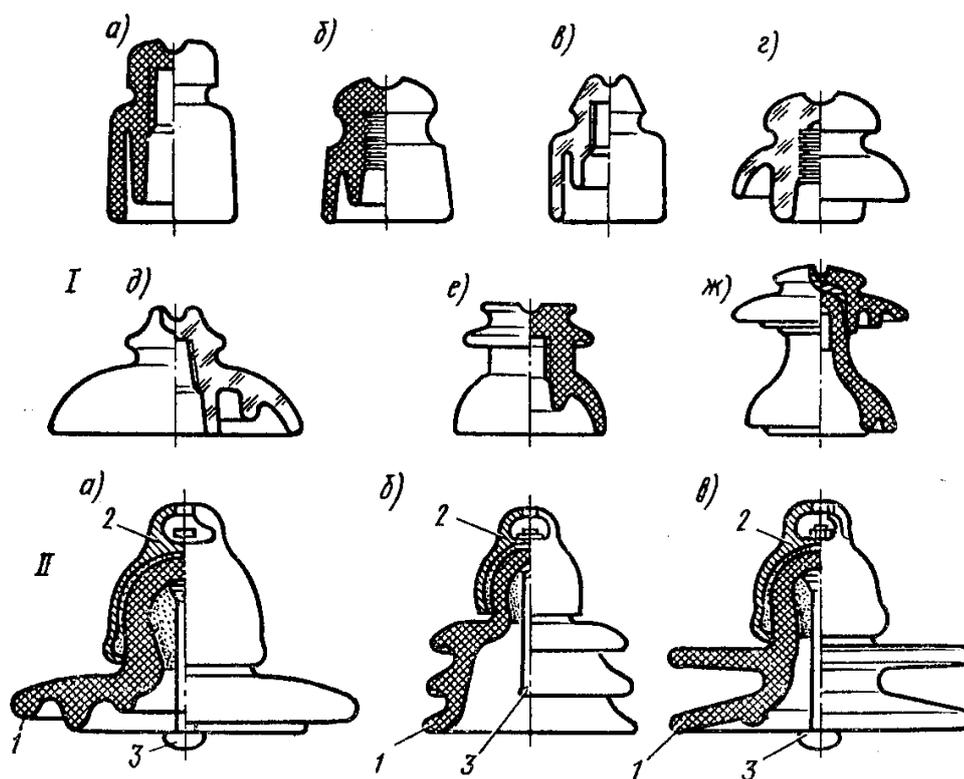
Изоляторы для ВЛ: I - штыревые: а - ТФ; б - ШФН; в - НС; г - ШС-10А; д - ШС-10В; е - ШФ-10Г; ж - ШФ-35Б; II - подвесные: а - нормальный (ПФ6-А); б, в - для загрязненных районов (ПР-3,5 и ПФГ6-А); 1 — изолирующая деталь (тарелка); 2 - шапка; 3 - стержень
